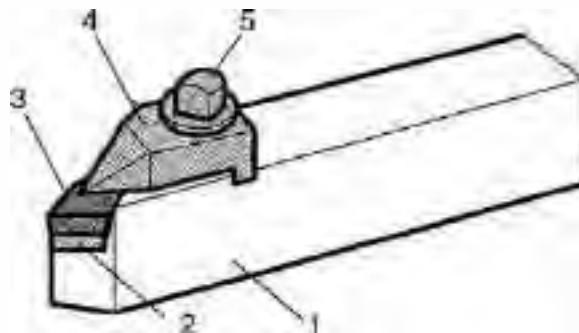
Нарізний різець з механічним кріпленням ромбичної пластинки з твердого сплаву
